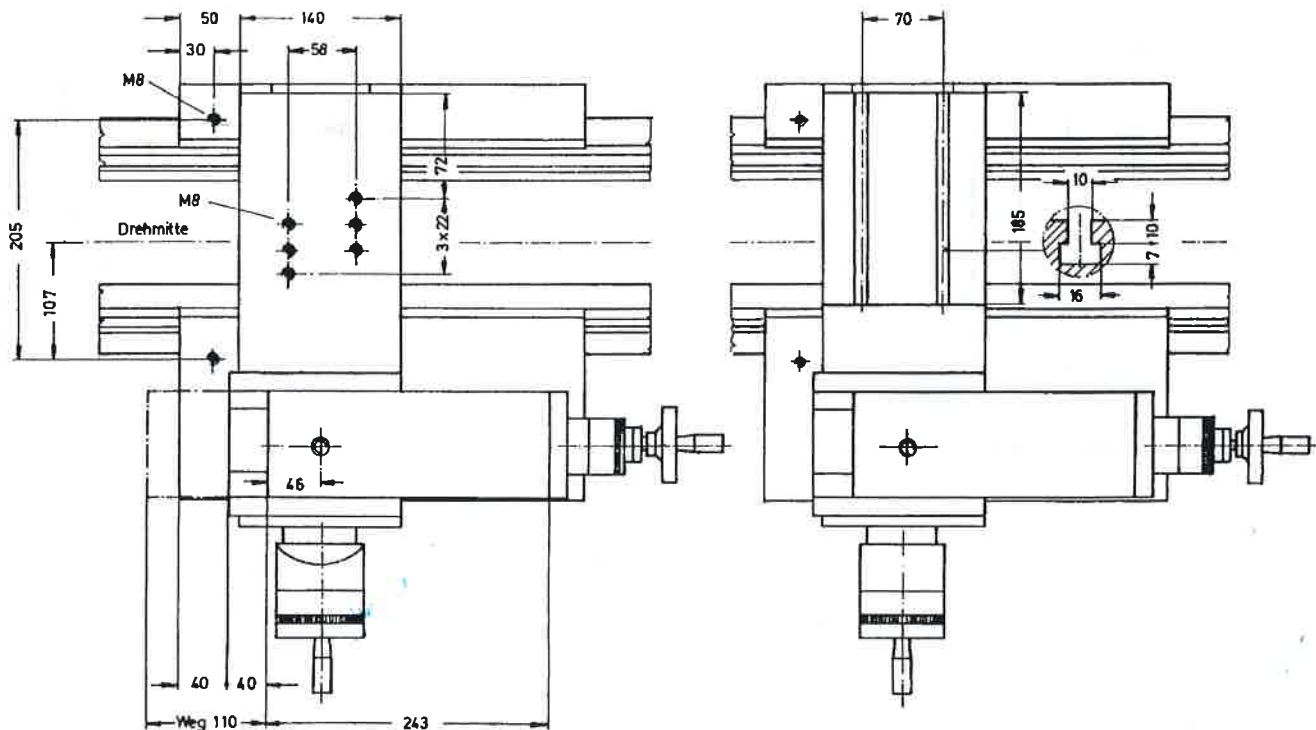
11: Anbaumaße Werkzeugschlitten und Werkzeugschlitten m.T-nut
